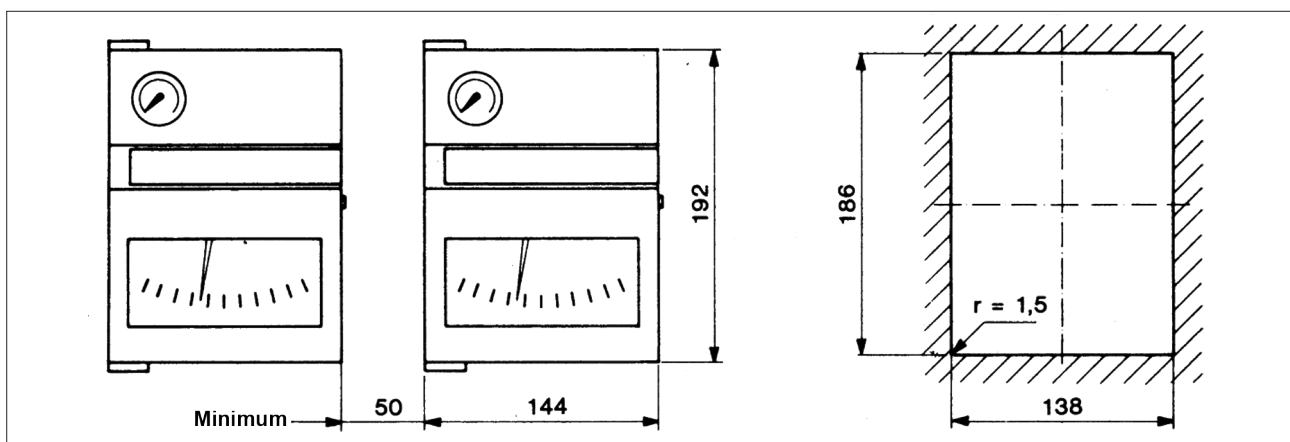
Abmessungen Frontausschnitt, Abstand Schalttafeleinbau
